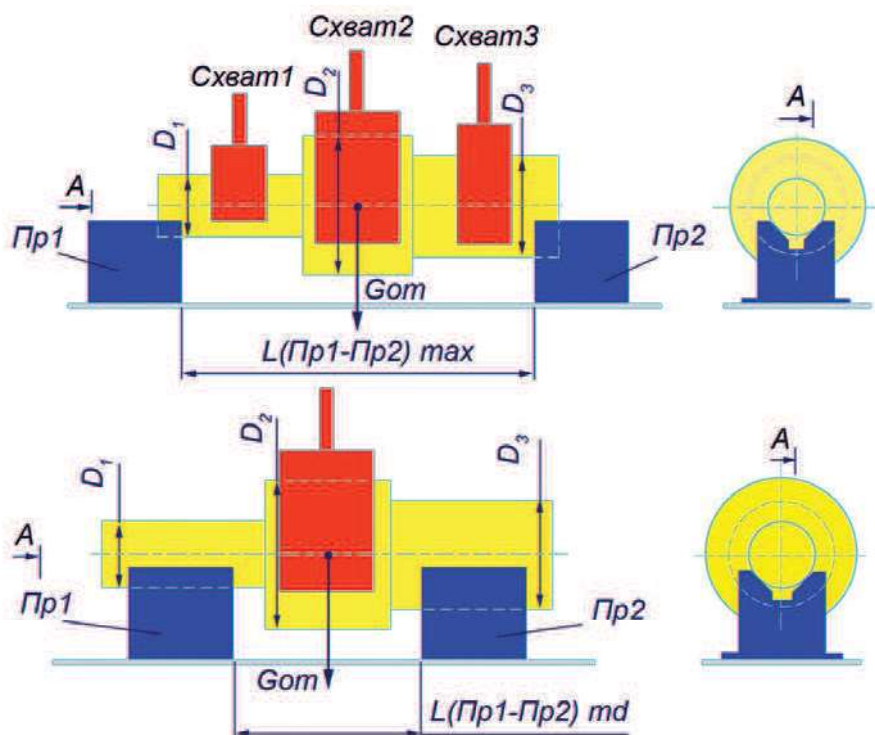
Примеры базирования цилиндрических ОМ (желтый цвет) в переналаживаемом приспособлении типа "призма" (синий цвет) с указанием возможных поверхностей базирования и закрепления ОМ в Сх ПР (красный цвет) при различном положении призм Пр1 и Пр2
